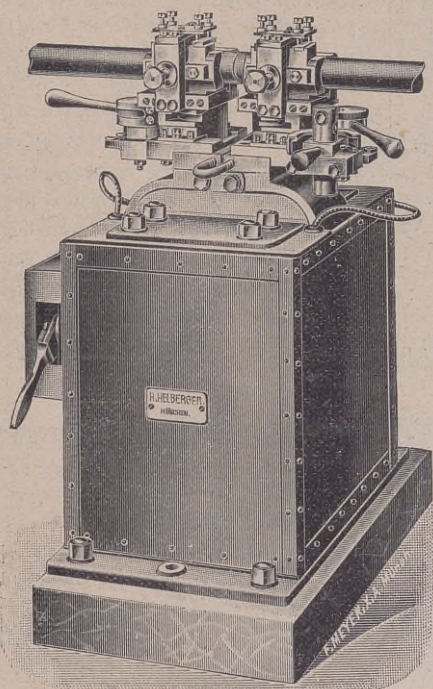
Elektrische Universalschweißmaschine Type II mit Rohraufsatz zum Schweißen von Röhren bis 100 mm<sup>2</sup> massiven Wandquerschnitts.
